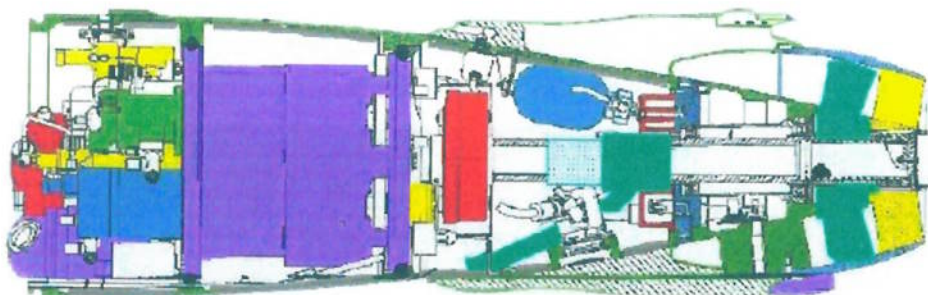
Lay-Out do motor a combustível Otto Fuel II.
